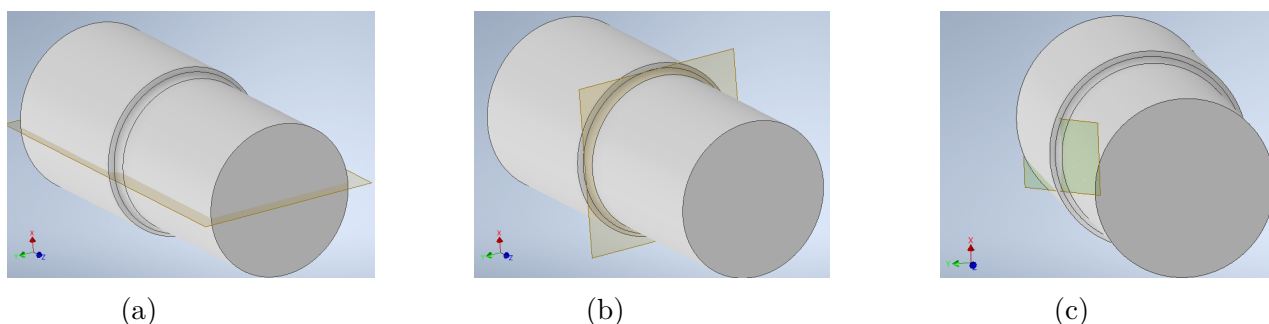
Plano Auxiliar 4, par do Plano de Referência (a); Plano Auxiliar 5, par do Plano Dorsal (b); Plano Auxiliar 6, par do Plano de Trabalho (c);
